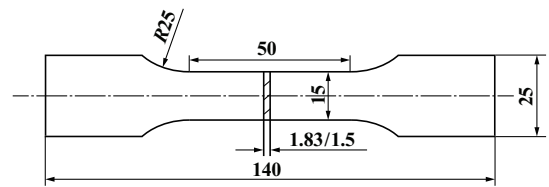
齿轮轴拉伸试样的尺寸(单位:mm)
